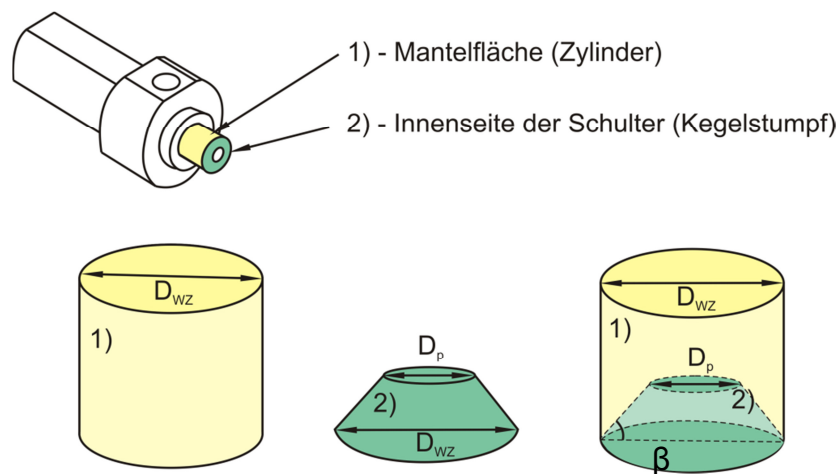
Darstellung des Schweißwerkzeugs als geometrisches Körper
